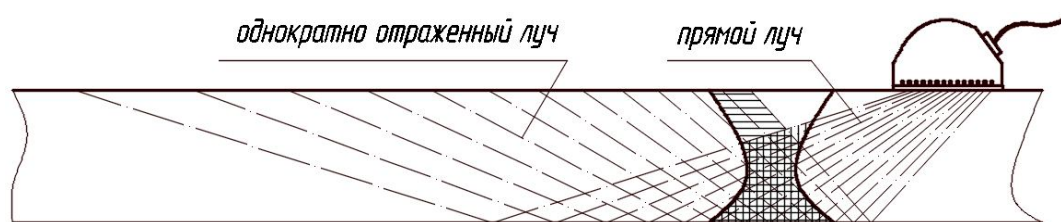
УЗ-контроль сварного шва с помощью технологии ФАР
